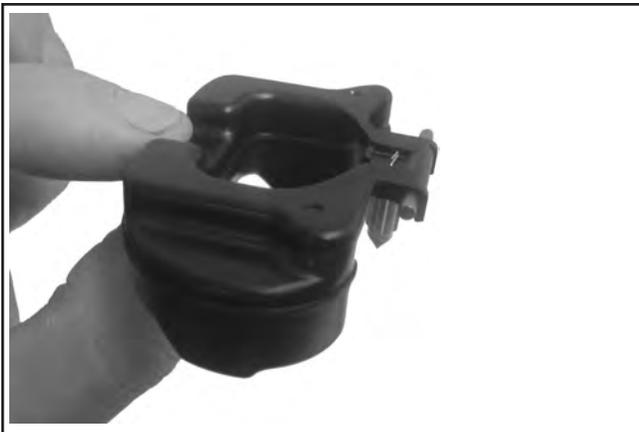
Details der Einlassnadel und des Schwimmers.
